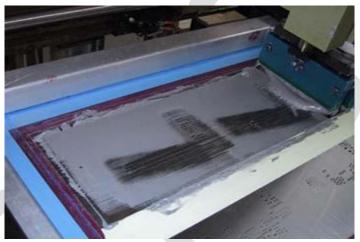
Dépôt de pâte pour soudure CMS.
